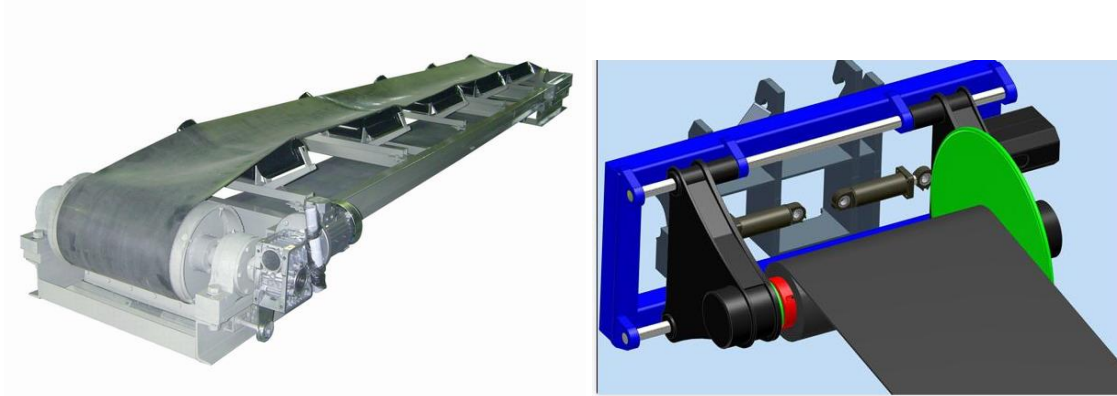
Загальний вигляд стрічкового конвеєра
